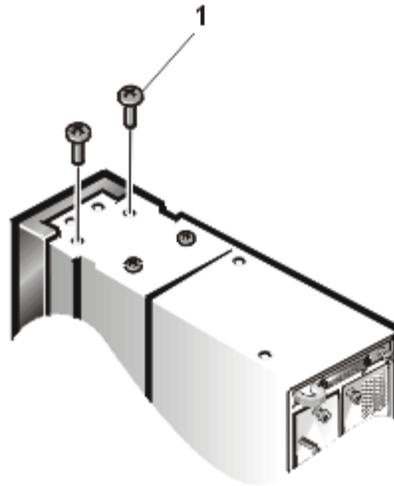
Desmontaje de la barra de bloqueo deslizante o de los tornillos de montaje de la tuerca-placa
